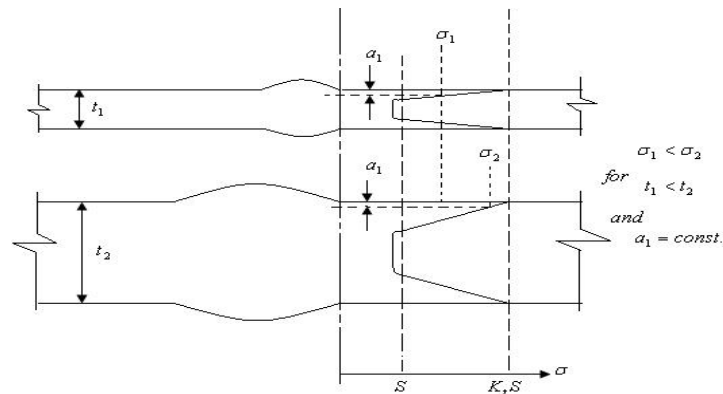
Modelo geométrico para el efecto del espesor de placa en la fatiga de uniones soldadas. Ref. [22]
